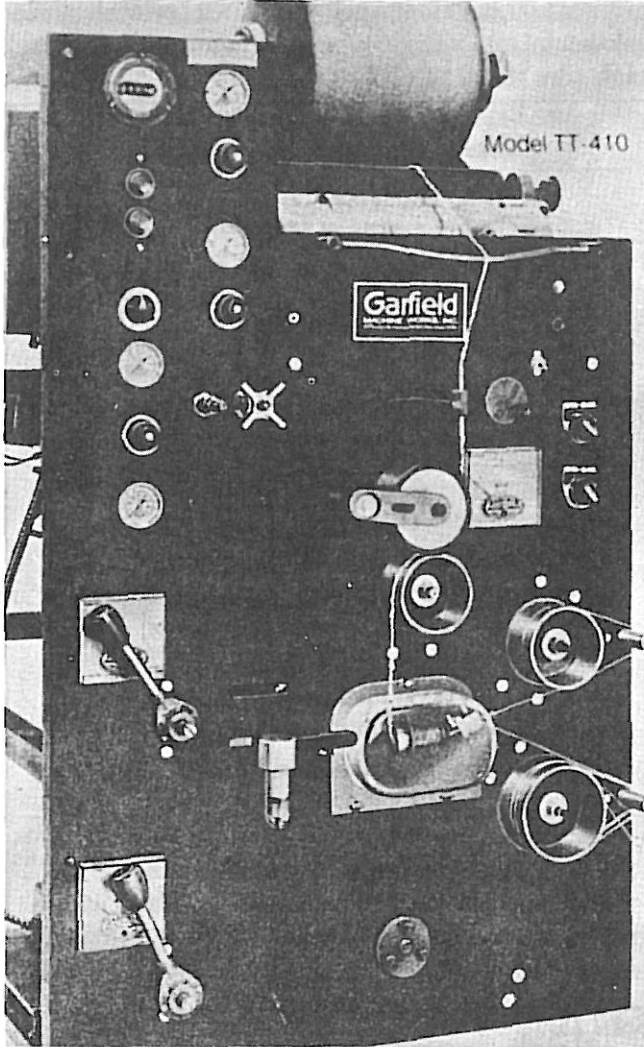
Hava Jetli Bir Tekstüre Makinası Olarak Dönüştürülmüş Büküm Makinası
